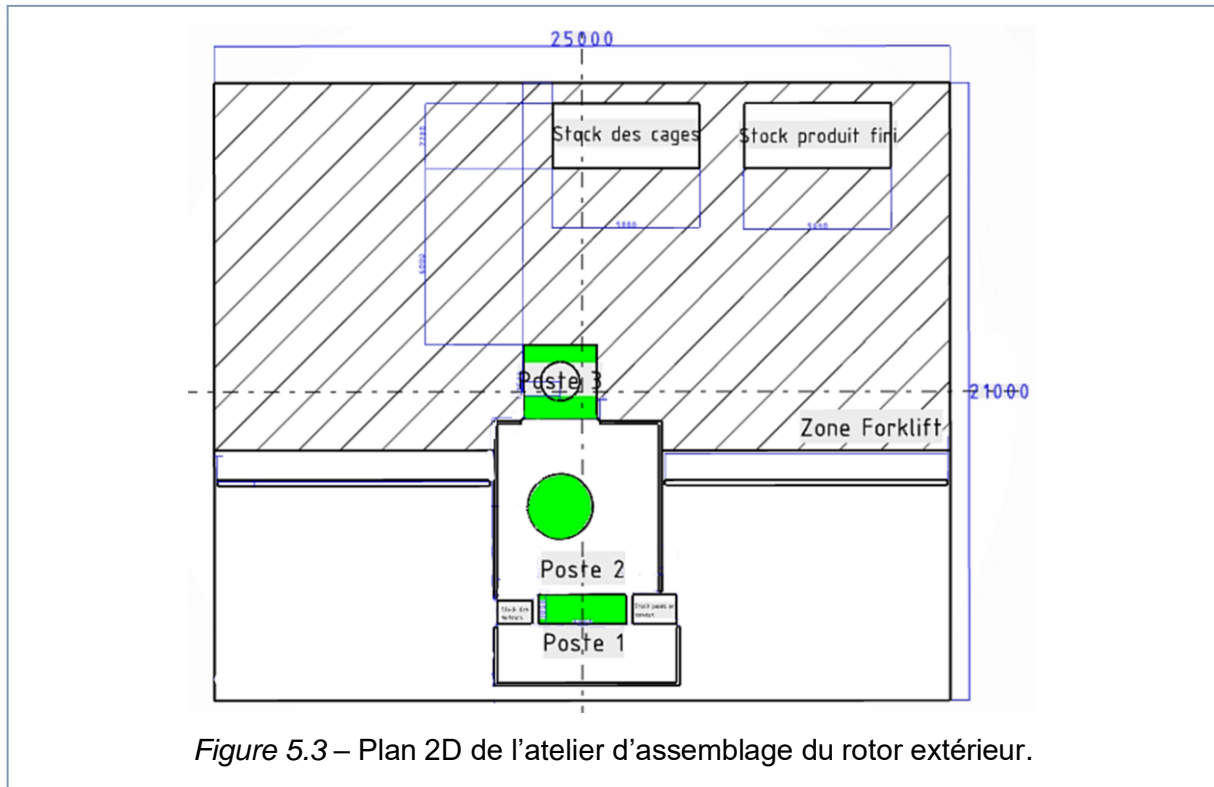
Plan 2D de l'atelier d'assemblage du rotor extérieur.
